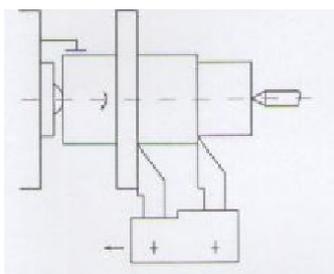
Обработка цилиндрических поверхностей вала за один переход
